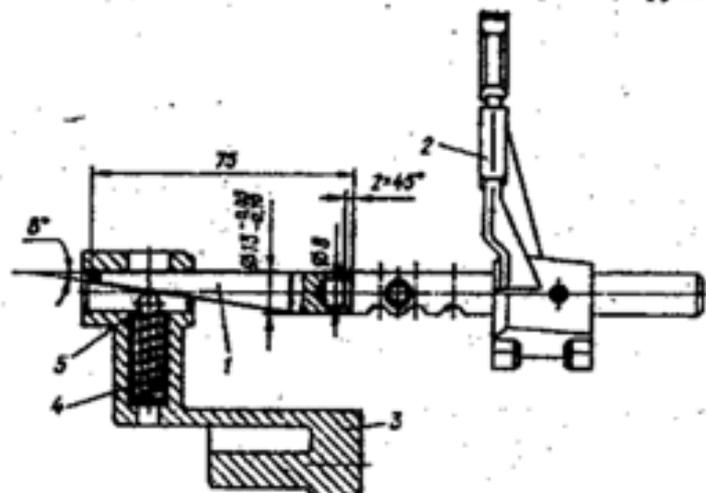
Установка штоков с вилками включения передач в корпус механизма переключения передач: 1 - оправка М9840-763; 2 - шток с вилкой включения третьей и четвертой передач; 3 - корпус механизма переключения передач; 4 - пружина фиксатора; 5 - шарик
